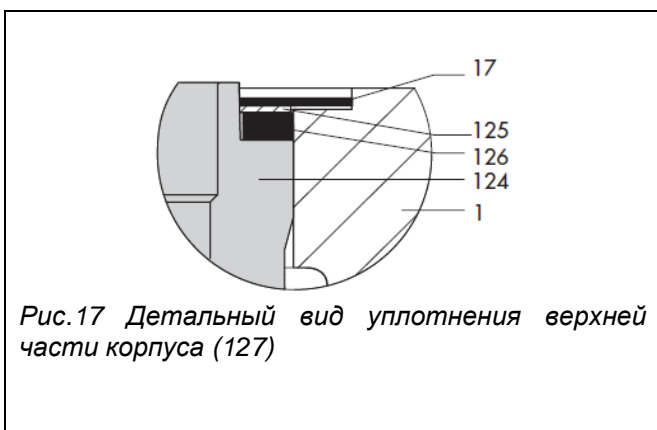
Детальный вид уплотнения верхней части корпуса (127)
